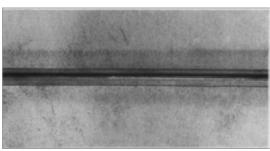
Stauchgrat(-wulst) einer Preßstumpfschweißung an einem Pkw-
